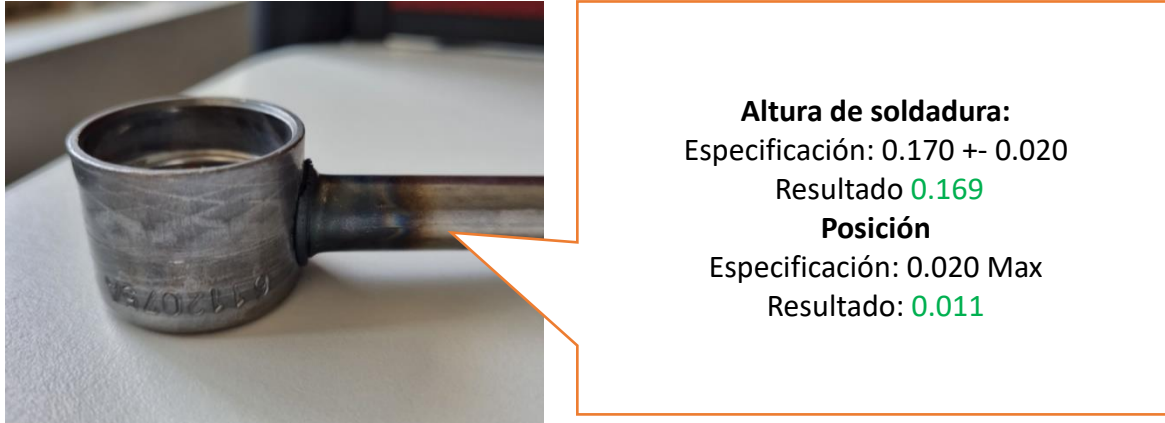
Proceso de soldadura con el uso del herramental.
